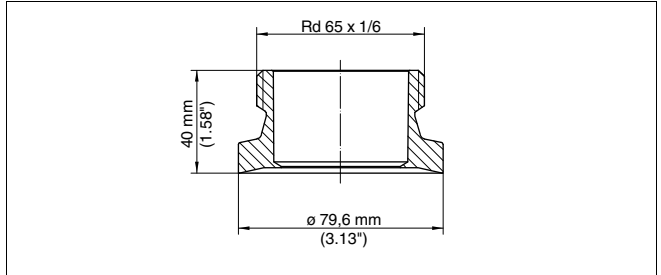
Maße Einschweißstutzen LA für Nutüberwurfmutter
